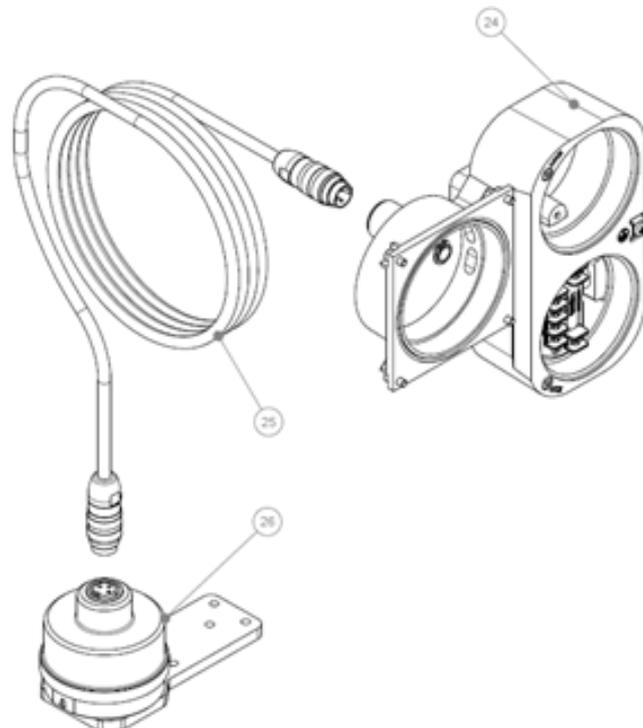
Desenho explodido do sensor remoto do VVP10.
